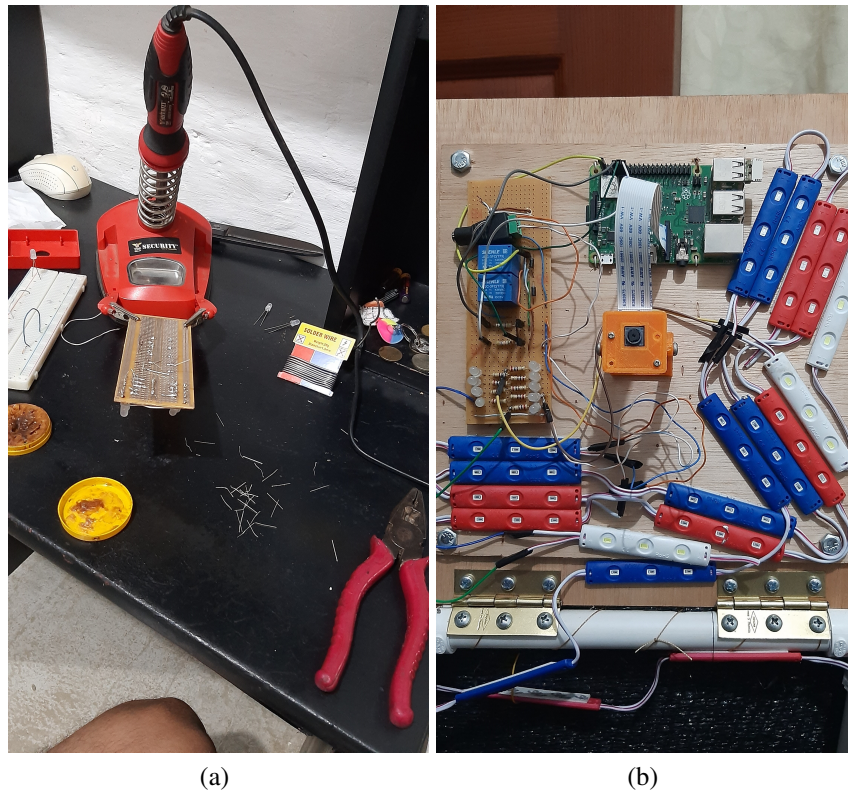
Proceso de soldadura y terminado del circuito - (a) Proceso de soldadura de los componentes del circuito en la placa de PCB, (b) Tabla de triplex montada con el circuito final.
